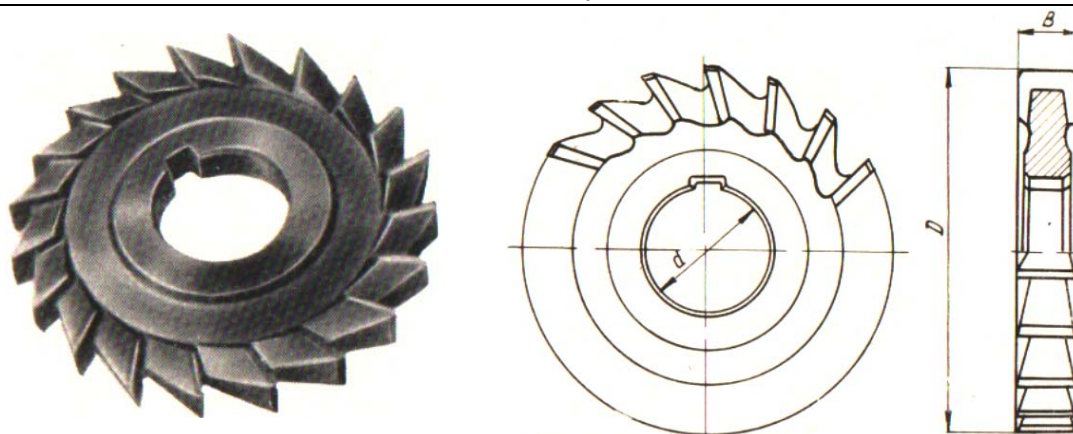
Современная конструкция цельной дисковой фрезы с торцевыми зубьями прямобочного профиля
